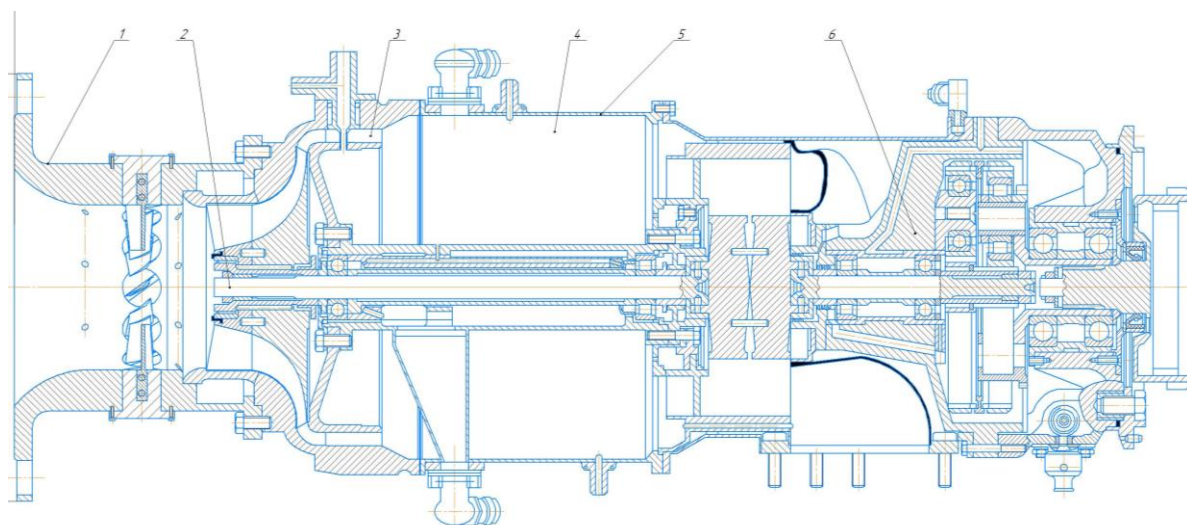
Сборочный чертеж ЦК с мультипликатором: 1 – ВНА; 2 – ротор; 3 – осевой лопаточный диффузор; 4 – сборная камера; 5 – корпус; 6 – мультипликатор
